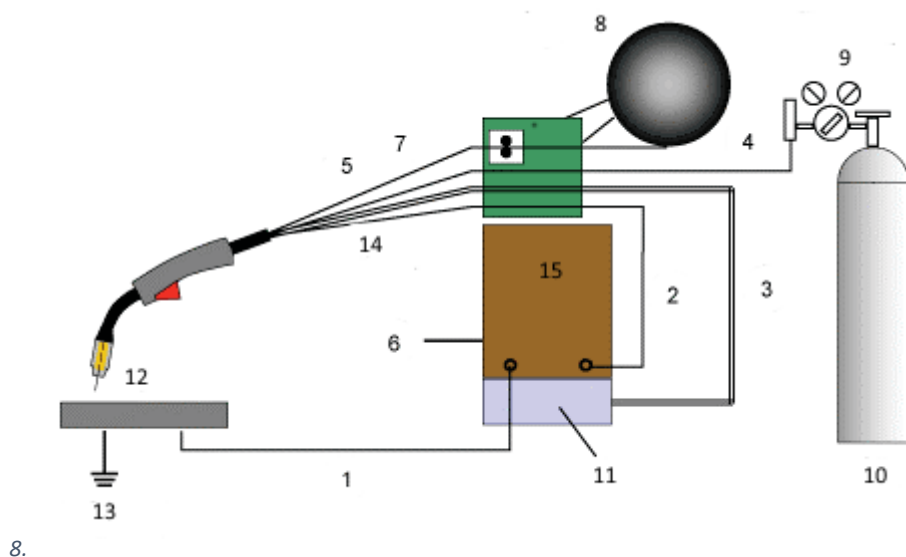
Representación esquemática de los equipos de soldadura MAG. Cable de retorno, 2. Cable de corriente de soldadura, 3. Entrada y salida de agua de refrigeración, 4. Gas protector del cilindro, 5. Electrodo de alambre en la camisa, 6. Energía de entrada primaria, 7. Circuito de interruptor de pistola, 8. Suministro de electrodo de alambre, 9. Regulador de gas protector y caudalímetro, 10. Suministro de gas protector, 11. 12. Unidad de refrigeración (opcional) Pistola de soldar o antorcha, 13. Tierra de seguridad (Consulte la guía HSE), 14. Conjunto de cables, 15. Fuente de alimentación. Fuente: TWI
